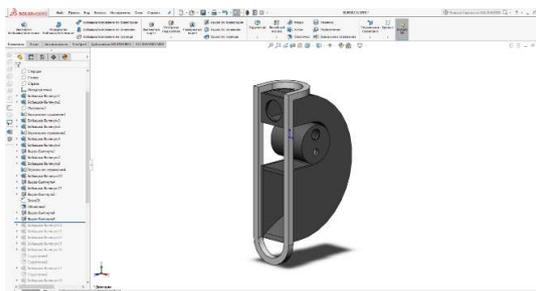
Добавление фазоинверторного корпуса для ВЧ/СЧ динамиков в трехмерный эскиз
